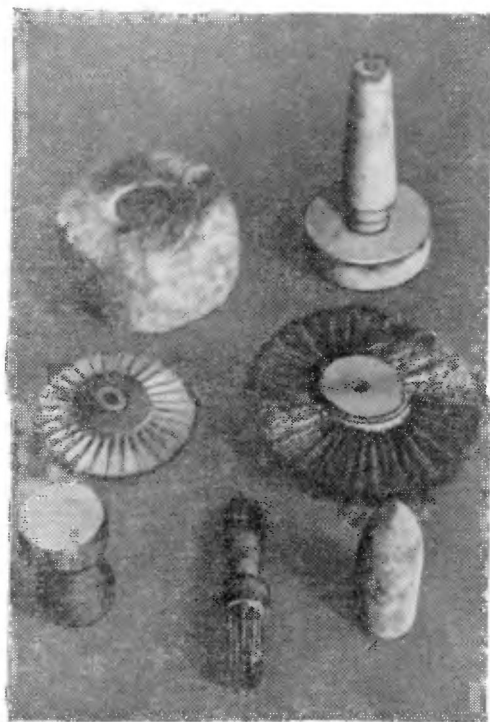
Различные инструменты для полировального станка: шерстяной круг, войлочный круг для колец (филец), круглая щетка для шлифования, латунная крацовка, полировальный фетр, щетка в виде кисти, полировальный конус (дори) из фетра
